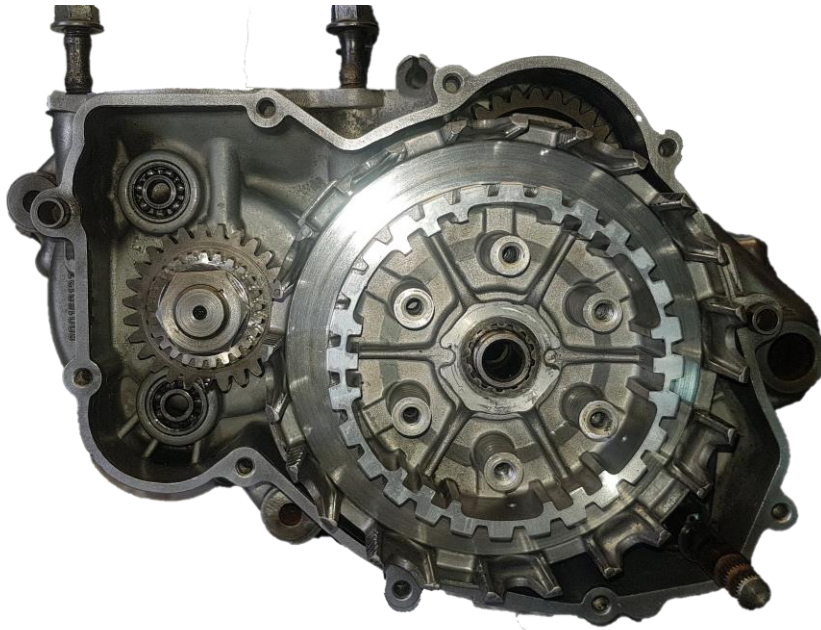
Vista del cárter izquierdo con la tapa retirada.
